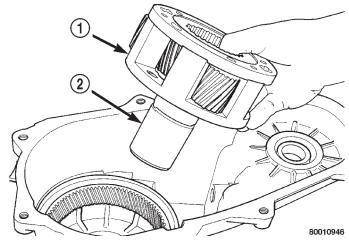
Desmontaje del engranaje impulsor y la caja de satélites
